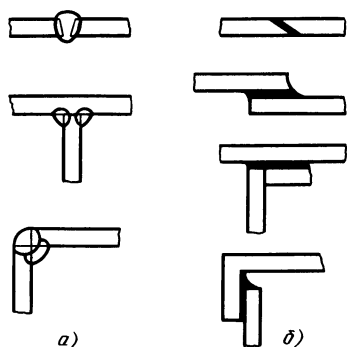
Конструктивные особенности соединений основных типов при сварке (а) и при пайке (б)
